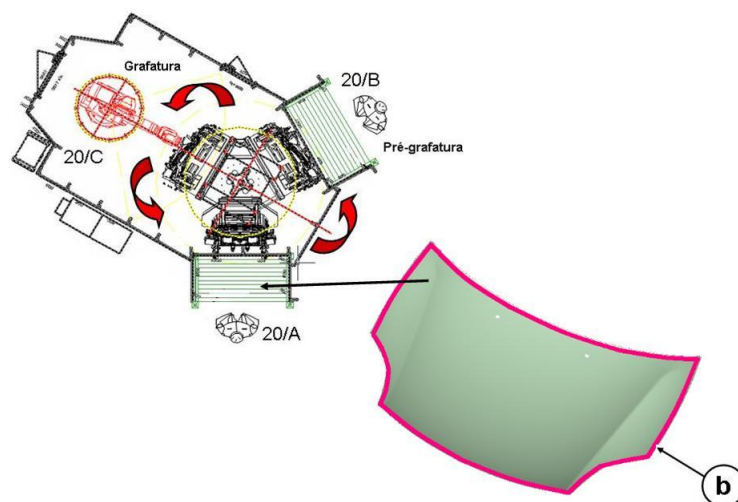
b – Adesivo aplicado no perímetro do capô. FONTE – FIASA
